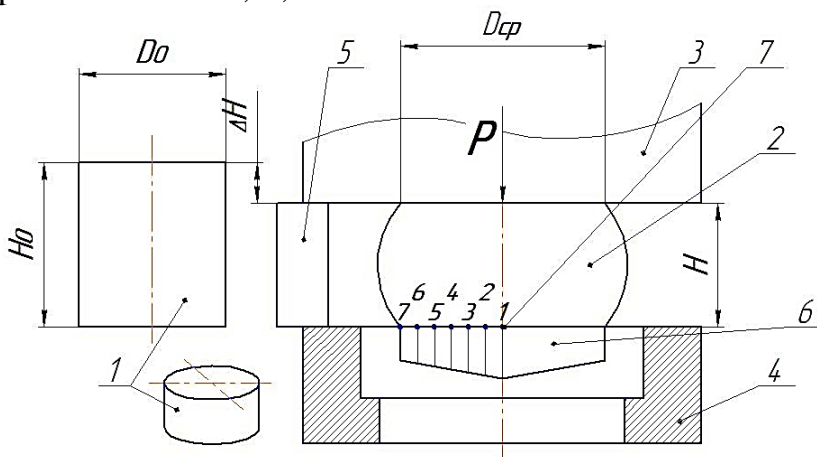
Схема осадки: 1-исходный образец; осаженный образец; 3-плита сплошная; 4-плита с щелью; 5-упор; 6-торцевой заусенец; 7-точки замера высоты заусенца.
